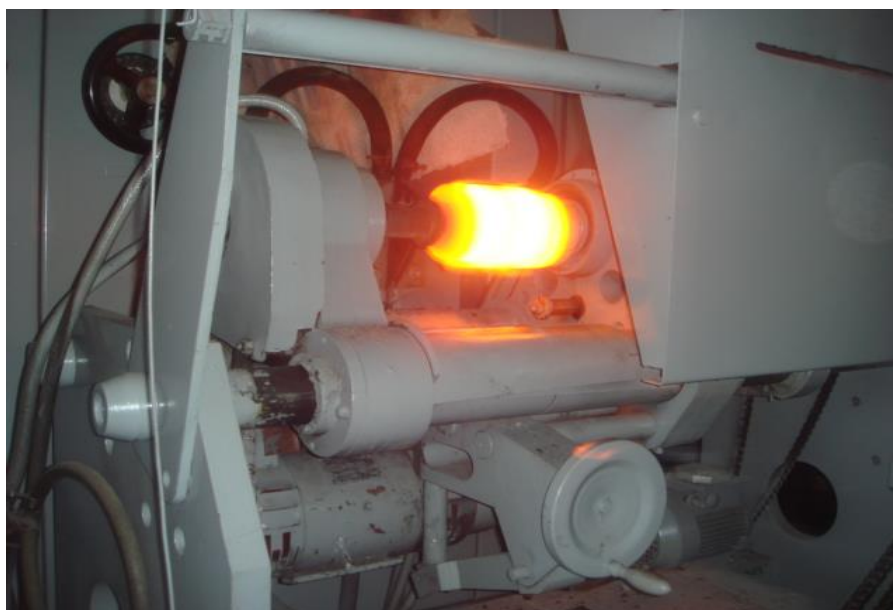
Процесс изготовления двухслойного антифрикционного изделия (биметаллической втулки подбивочного блока выправочно-подбивочно-рихтовочной машины ВПР)
